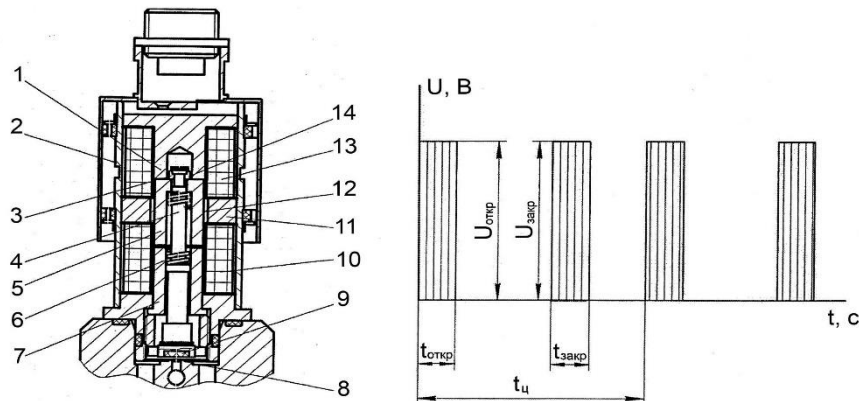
а – конструктивна схема клапана: 1 – верхній стоп; 2 – корпус клапана; 3 – шийка штока; 4 – шток; 5 – повзун (якір); 6 – пружина; 7 – нижній стоп; 8 – сідли; 9 – золотник з гумовою вставкою; 10 – нижня обмотка; 11 – постійний магніт; 12 – трубка розділова; 13 – верхня обмотка; 14 – шайба стопорна; б – форма керуючих електричних імпульсів
